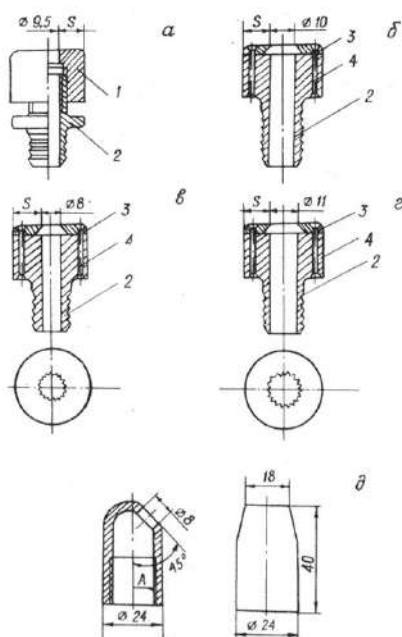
Насадки для лабораторно-полевой установки: 1 - головка; 2 – штуцер; 3 – кольцо; 4 - заклепка
